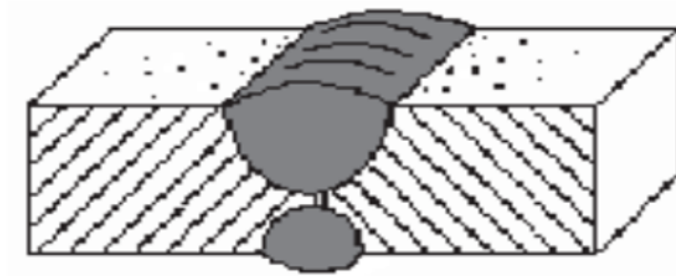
Эскиз дефекта сварного шва
